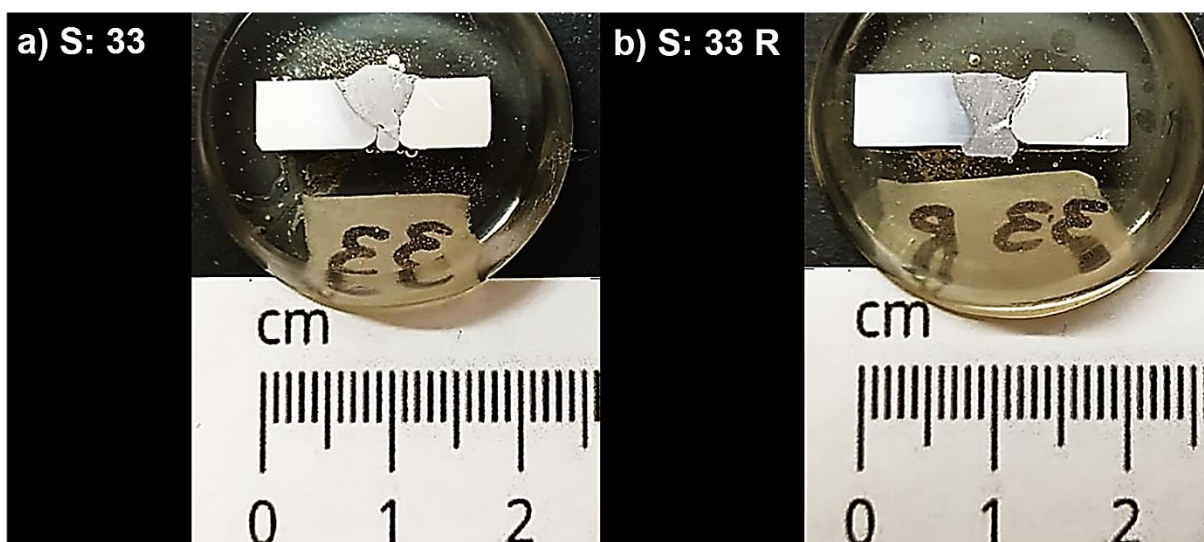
77 Soldadura 33 y soldadura 33 R montadas en resina epóxica con acabado espejo y atacadas con reactivo Keller.
